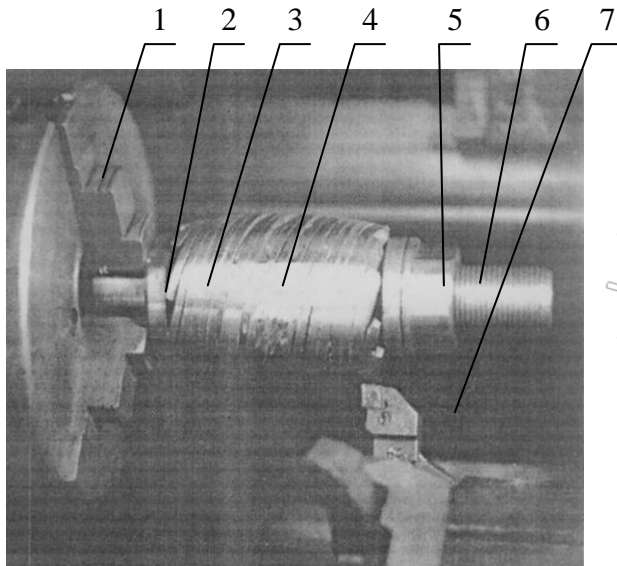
Процес чорнового профілювання гвинтових заготовок на токарному верстаті з ЧПК:
